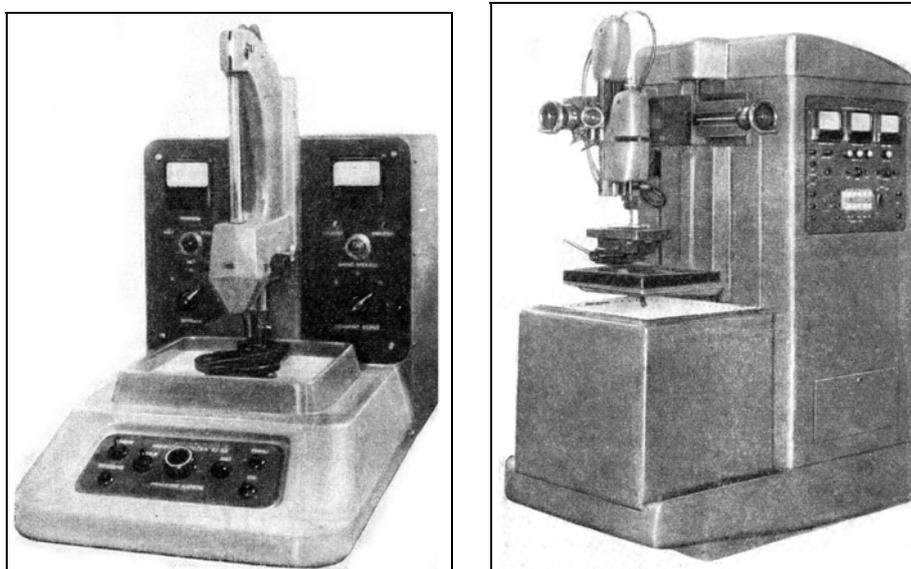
Внешний вид электроискровой установки для изготовления отверстий малого диаметра (слева) и установка для изготовления крупных деталей (Чехословацкая республика).
